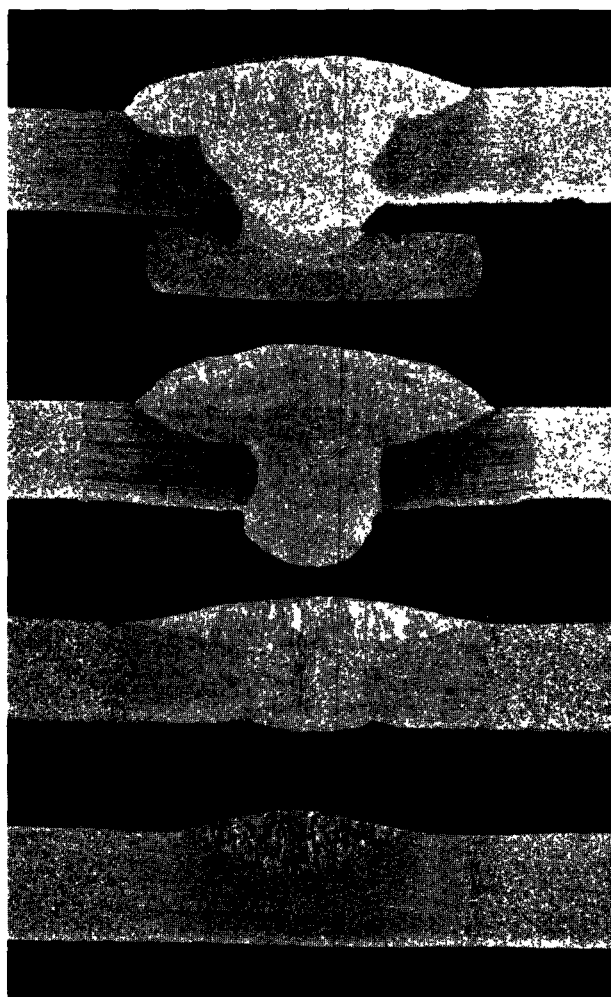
Sections transversales des éprouvettes montrant le profil caractéristique des cordons de soudure obtenus avec les divers modes opératoires employés pour la première passe: de haut en bas: bague support; électrode B (enrobage cellulosique); T.I.G.; soudure simulée (sans première passe).
